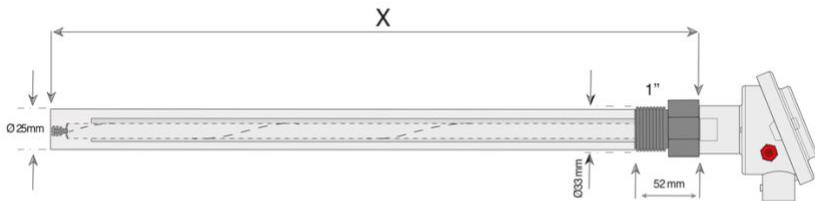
CarboProbe™ HT PRO mit 1"-Gewinde und doppeltes Keramikschutzrohr.
